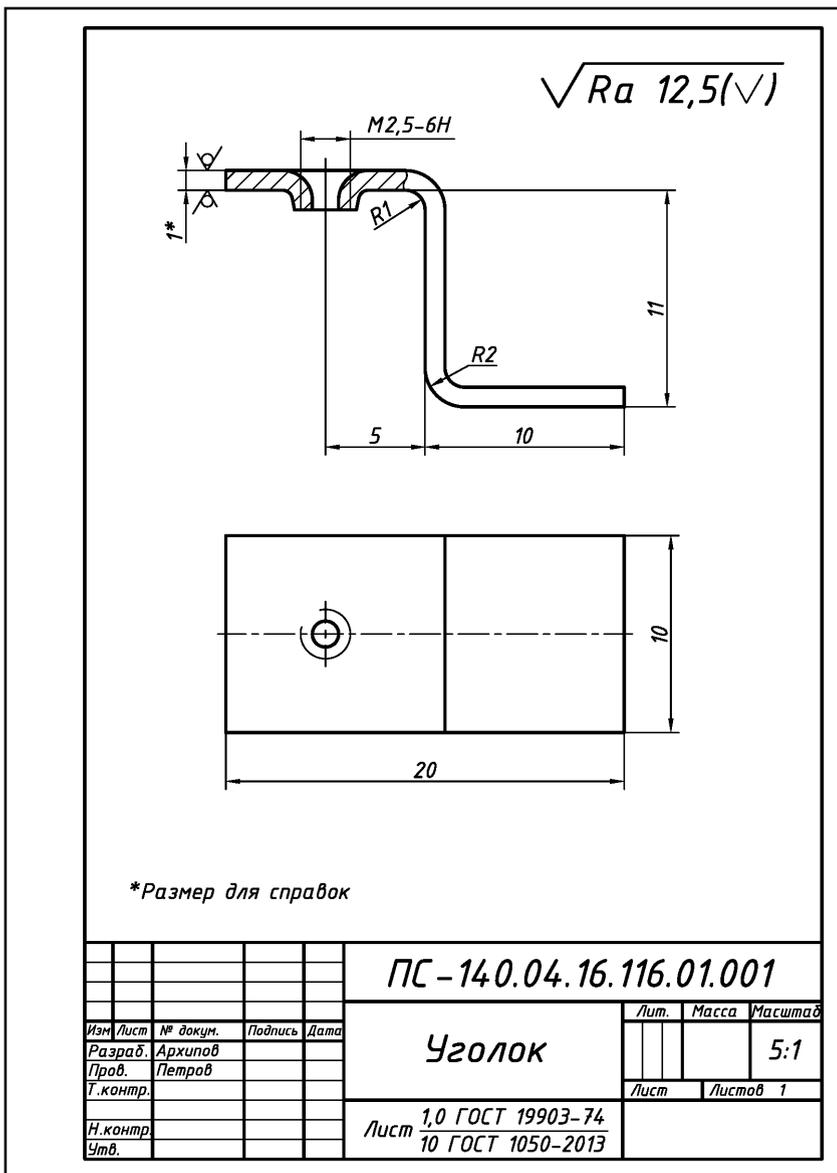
Оформление рабочего чертежа детали «Уголок»
